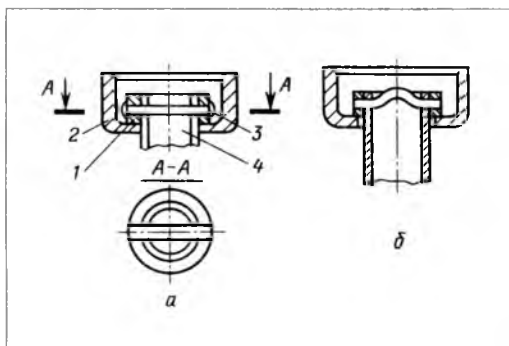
Крепление кольца на трубке излива с помощью штифта: а — с расклепкой концов штифта; б — изгибом середины штифта (1 — кольцо; 2 — накидная гайка; 3 — штифт; 4 — трубка)
